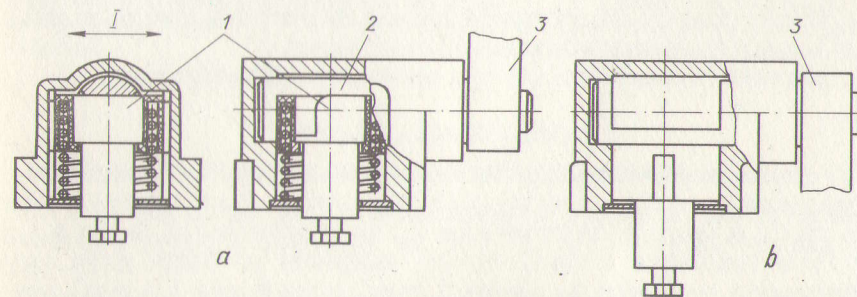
Привод рычаг с роликом: 1 — толкатель; 2 — вал; 3 — рычаг; I — рабочий ход
